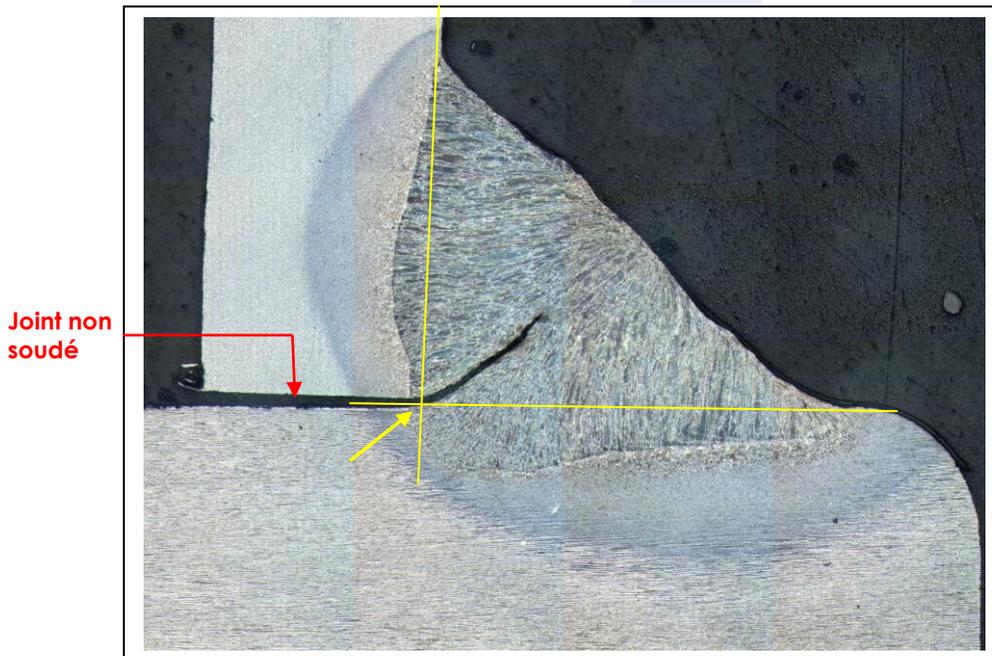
Fissure à la racine du cordon de soudure 2DI - surface ext.
